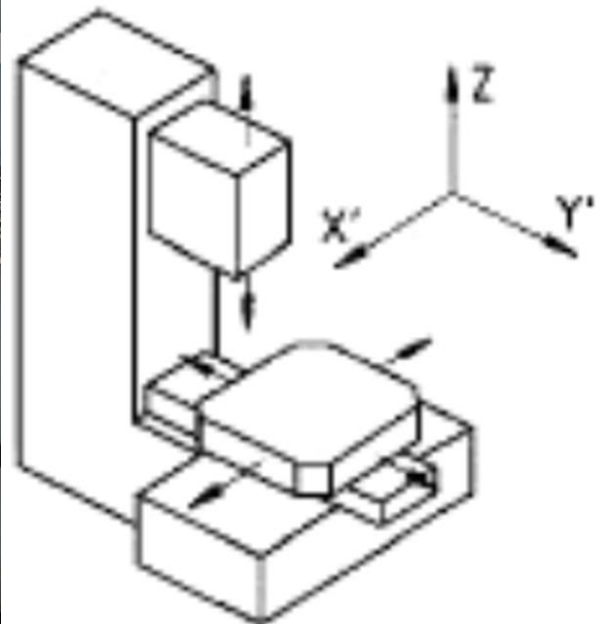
Внешний вид станка, компоновка и расположение осей
